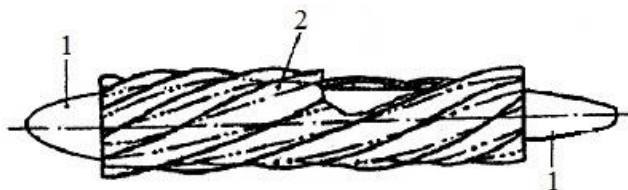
Транспортная машина с винтовым движителем и напусками условно цилиндрической формы (вид сбоку)
